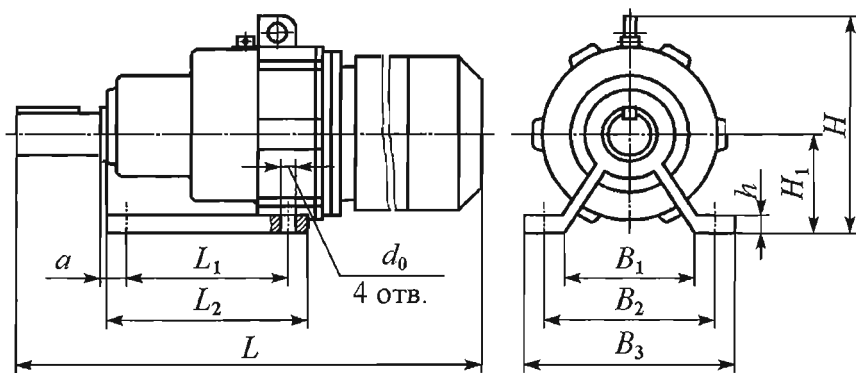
Габаритные, установочные и присоединительные размеры редуктора
